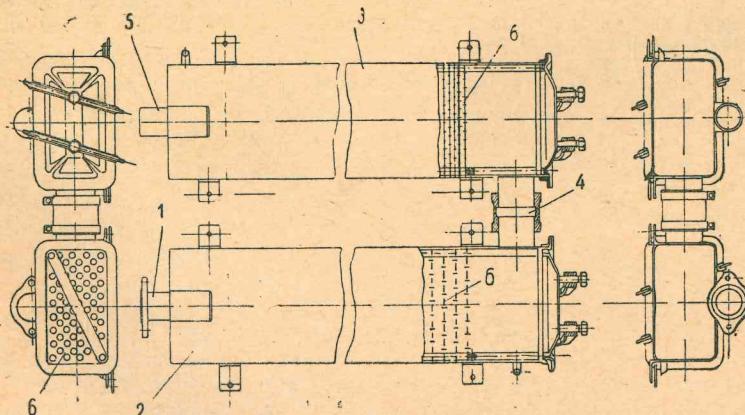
Инерционный газоочиститель установки НАТИ-Г-14
